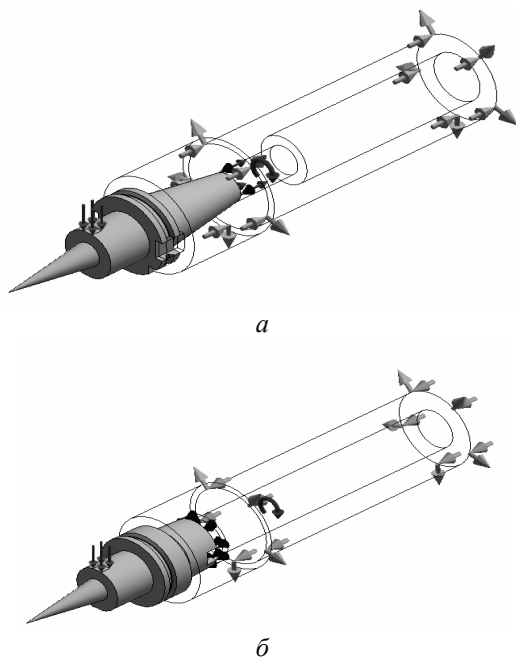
Твердотельные сборки шпинделя с оправками для выполнения расчёта: а – SK; б – HSK
